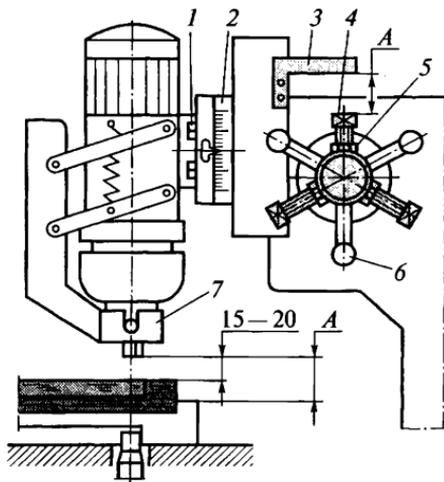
Настройка ограничителей хода суппорта фрезерного станка:
